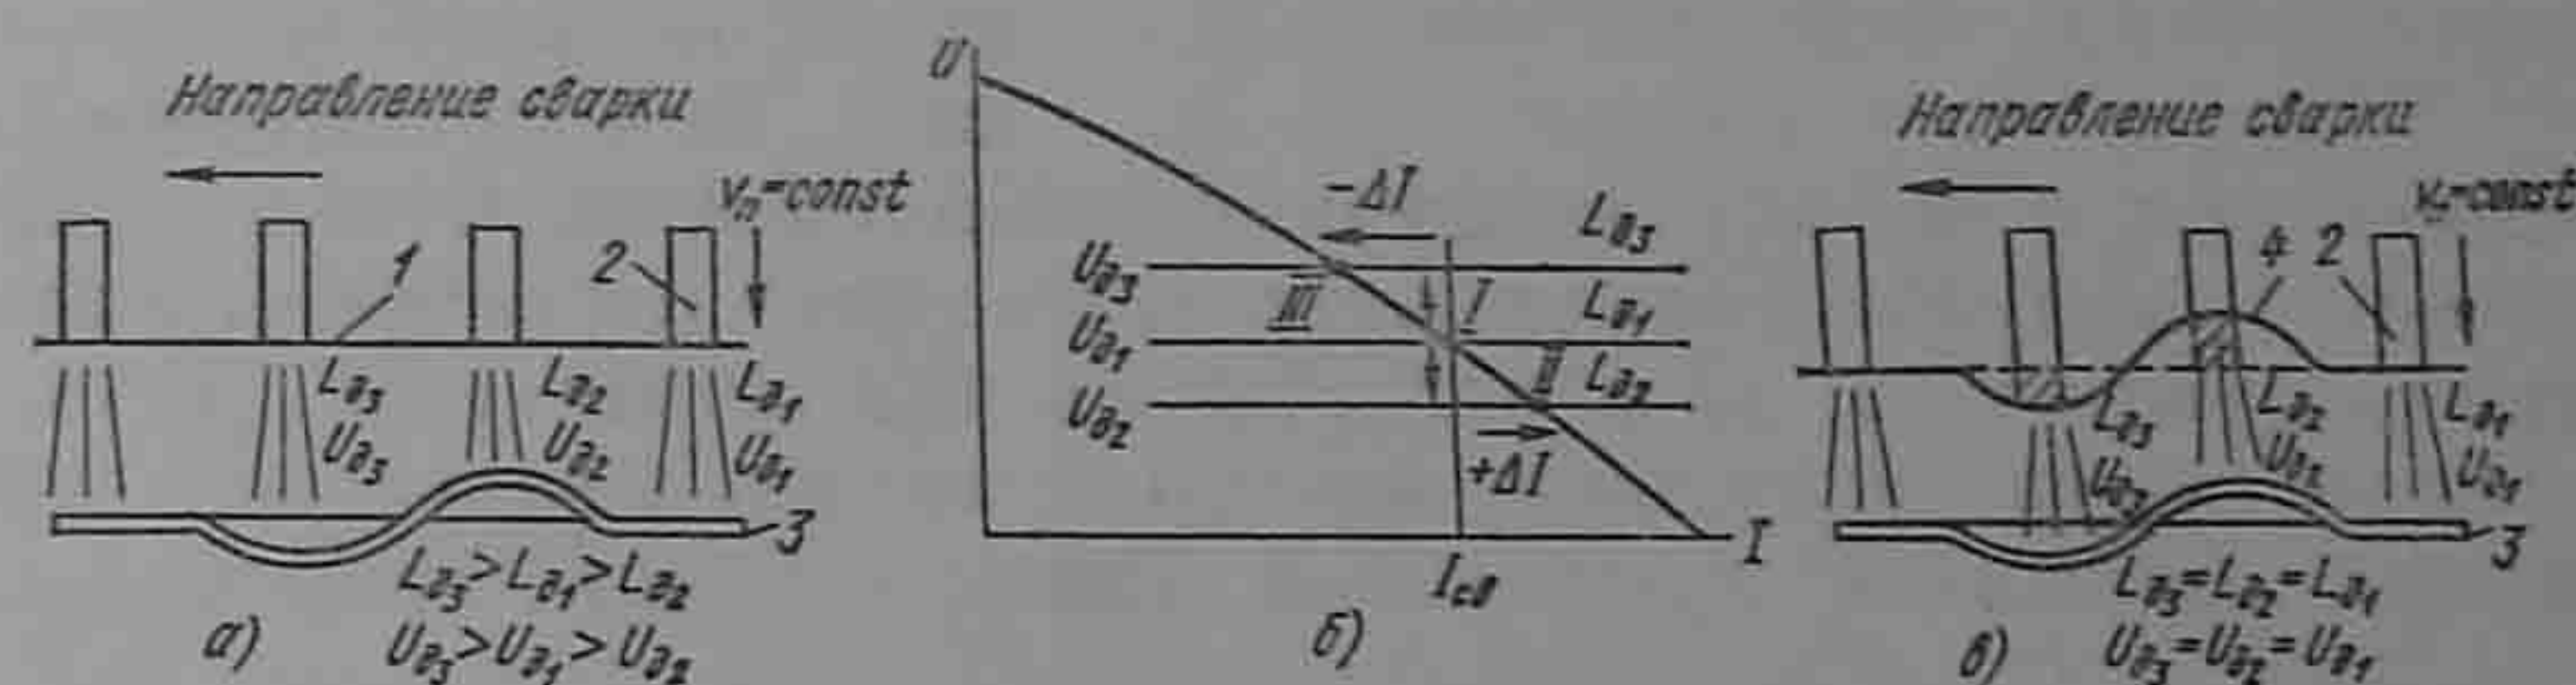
Процесс саморегулирования дуги при сварке листа с неровной поверхностью
